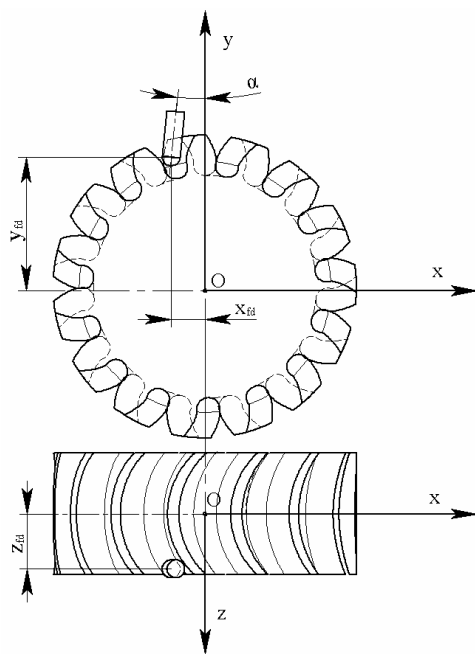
Текущее положение пальцевой фрезы при нарезании арочного зуба на 5-ти координатном станке
